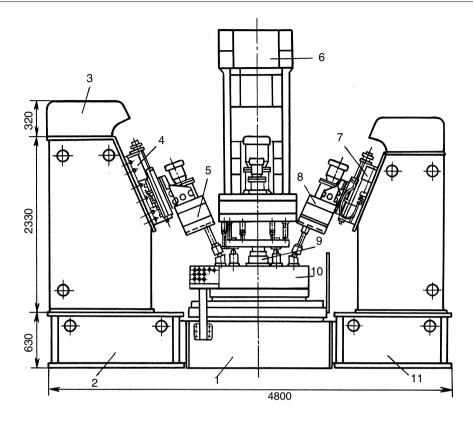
Основные узлы агрегатного станка: 1— сварное основание; 2, 11— подставки; 3— наклонные стойки; 4, 7— силовые стола со шпиндельными головками 5 и 8; 6— вертикальные стойки; 9— зажимное приспособление; 10— поворотный делительный стол
